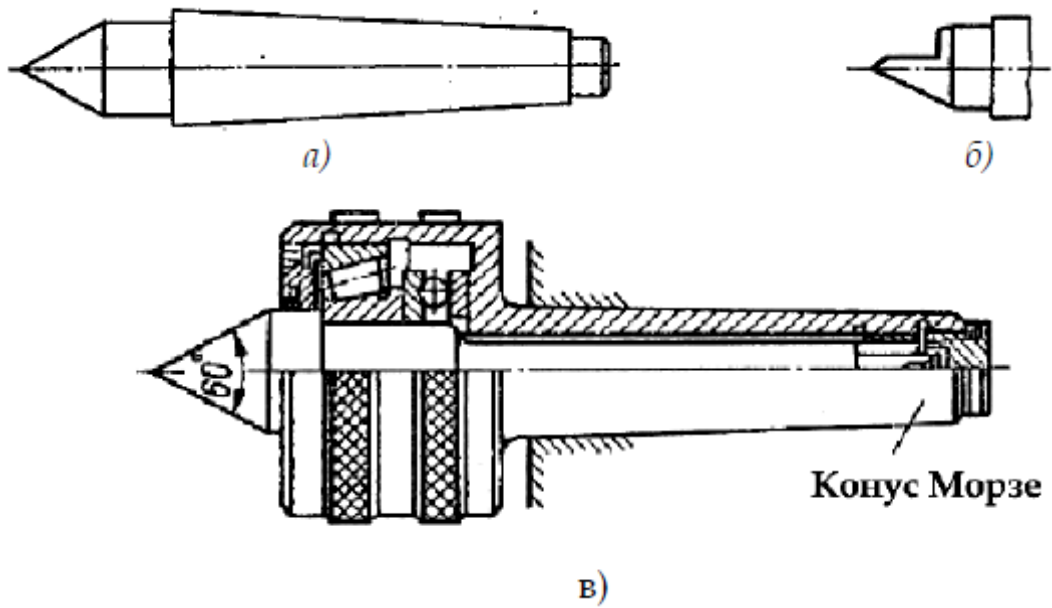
Центри: а – звичайний центр; б – півцентр; в – обертовий центр
